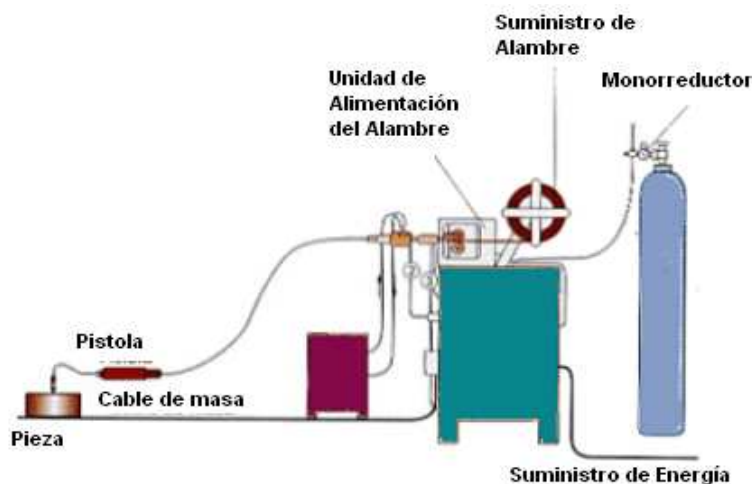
Equipo necesario para la soldadura bajo protección de gas con alimentación de electrodo sólido
